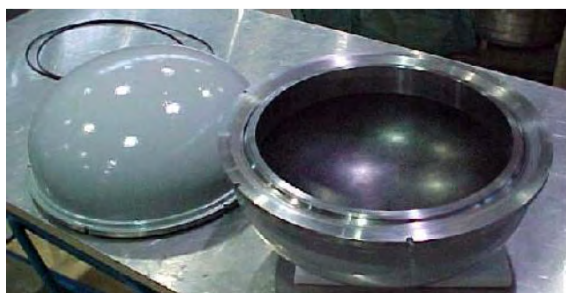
Сформированная методом пропитки под вакуумом углепластиковая крышка для цилиндрического прочного корпуса [6]
